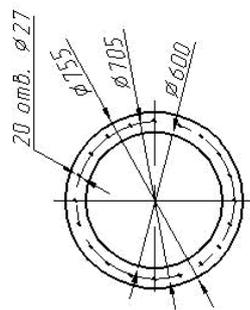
Габаритные размеры газодувки 2ТГ-500-1,08,
